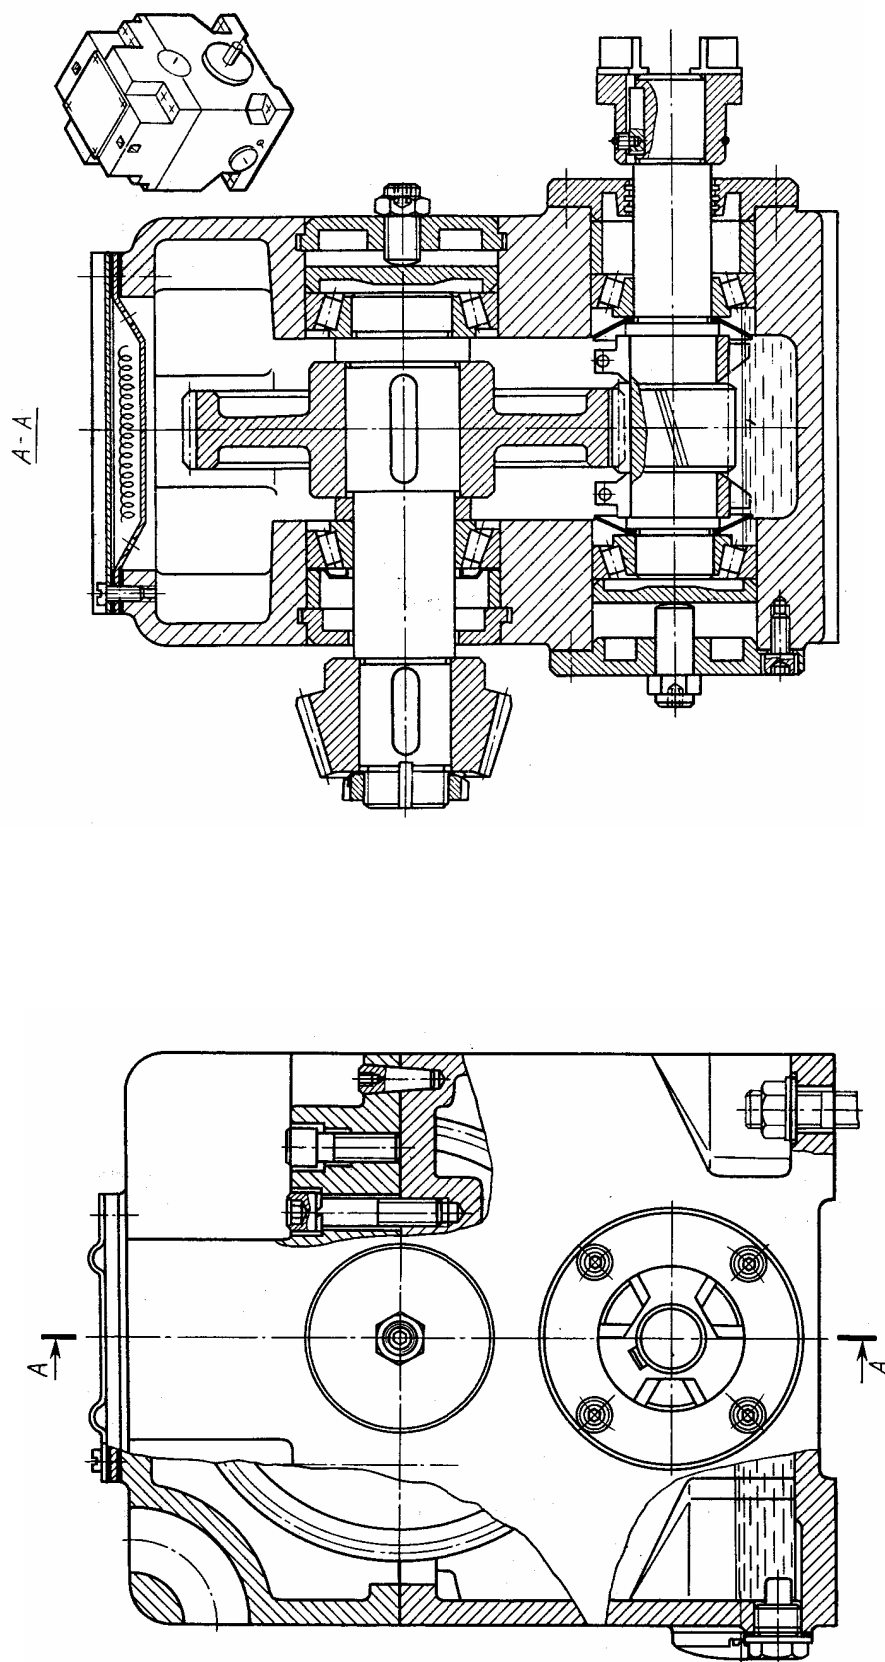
Редуктор (А15) цилиндрический одноступенчатый вертикальный с нижним расположением шестерни
